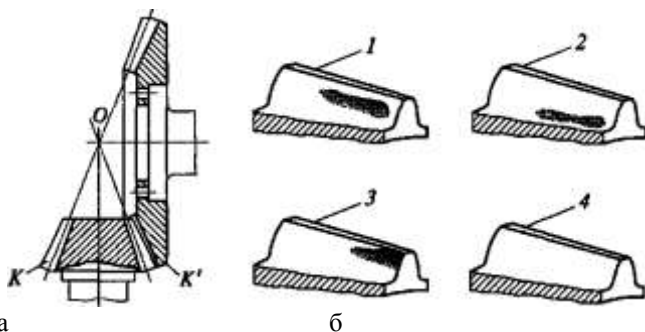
Регулировка зацепления зубьев колес (а) и отпечатки краски при проверке качества зацепления (б) конической зубчатой передачи:
